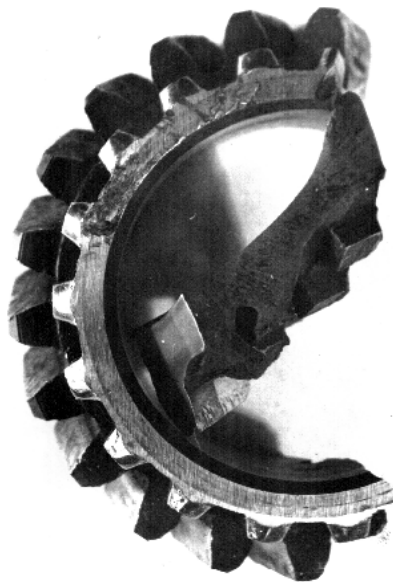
Общий вид разрушенной шестерни реверс-редуктора
